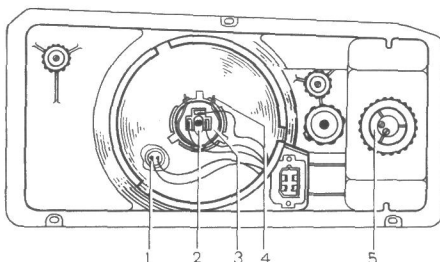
Замена ламп в блок-фаре: 1 — патрон лампы стояночного света; 2 — колодка; 3 — патрон с лампой фары в сборе; 4 — пружинный фиксатор; 5 — патрон лампы указателя поворота
